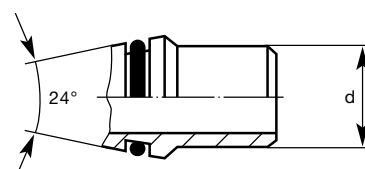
Резьбовой штуцер с конической уплотнительной поверхностью 24°: форма А для приварного соединения
